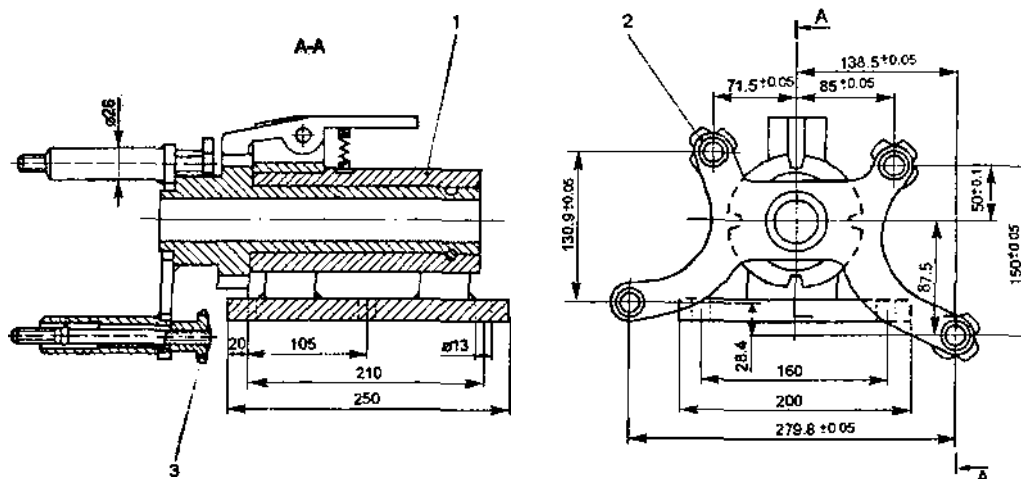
Приспособление М9832-345 для крепления двигателя при разборке и сборке:
